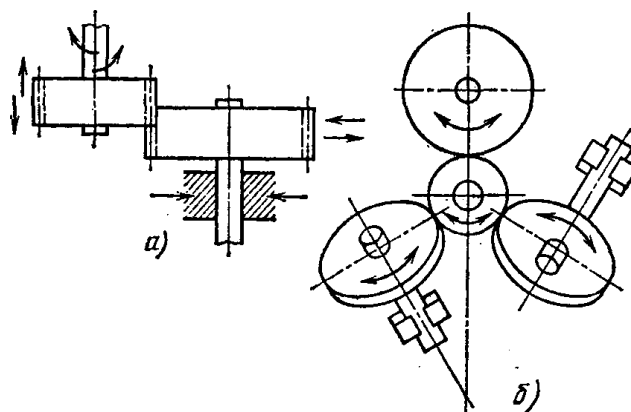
Схеми притирки зубів циліндричних зубчастих коліс
